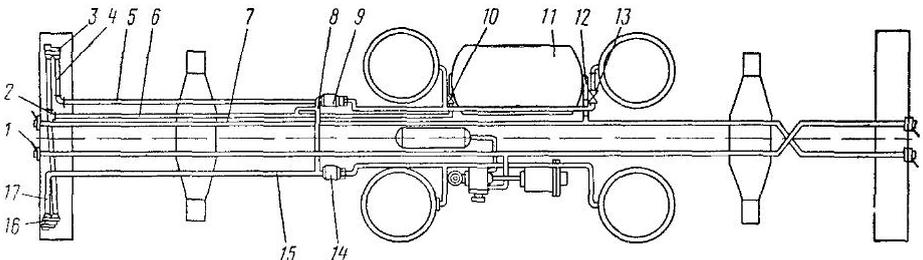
Установка пневматического оборудования вагона-самосвала ЗВС-50
